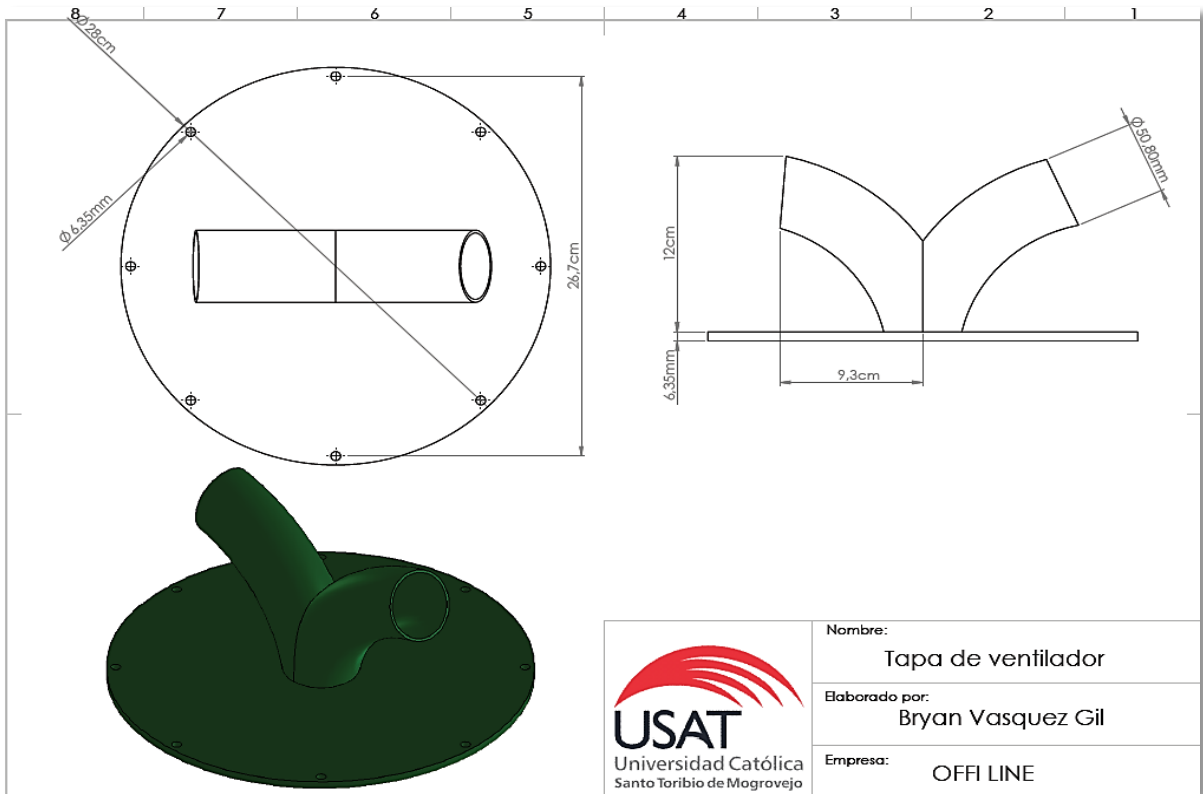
Planos de la estructura del tubo de conexión y la vista general
